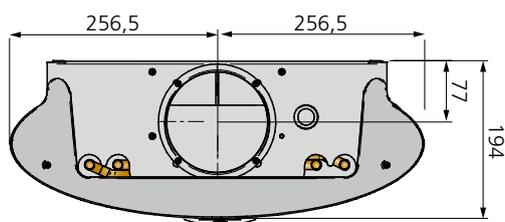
Dimensions WISE Adriatic Ellips, vue arrière du raccordement aéraulique
